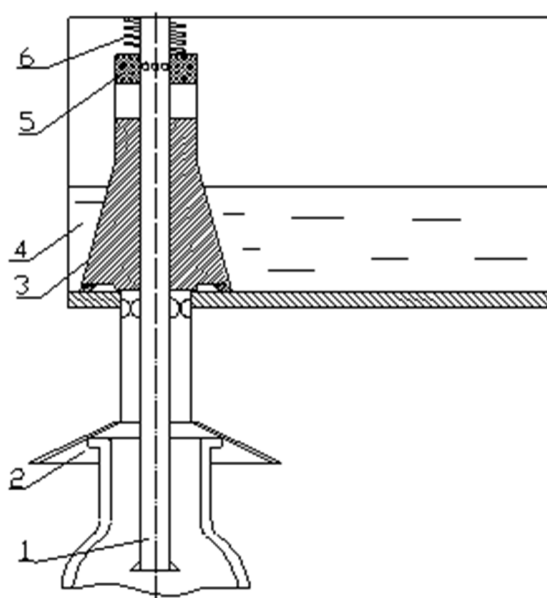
Схема однокамерного фасувального пристрою: 1 – газова трубка; 2 – дзвіночок із зливною трубкою; 3 – рідинний клапан; 4 – резервуар; 5 – газовий клапан; 6 – пружина
